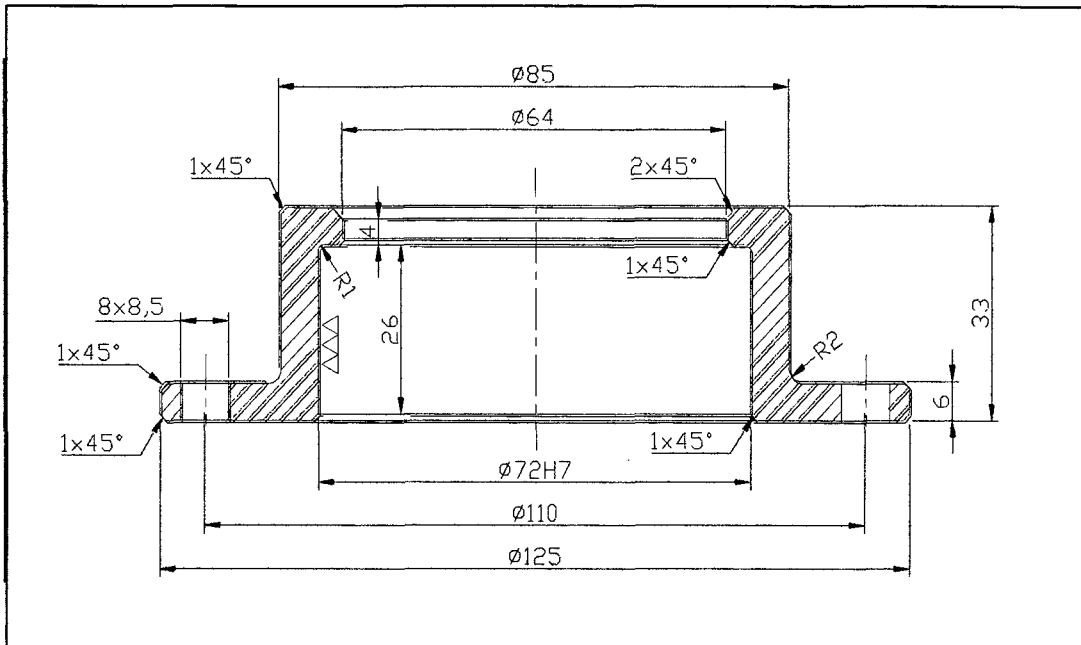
Peça em 2D desenhada em CAD com dimensões e informações de usinagem.
